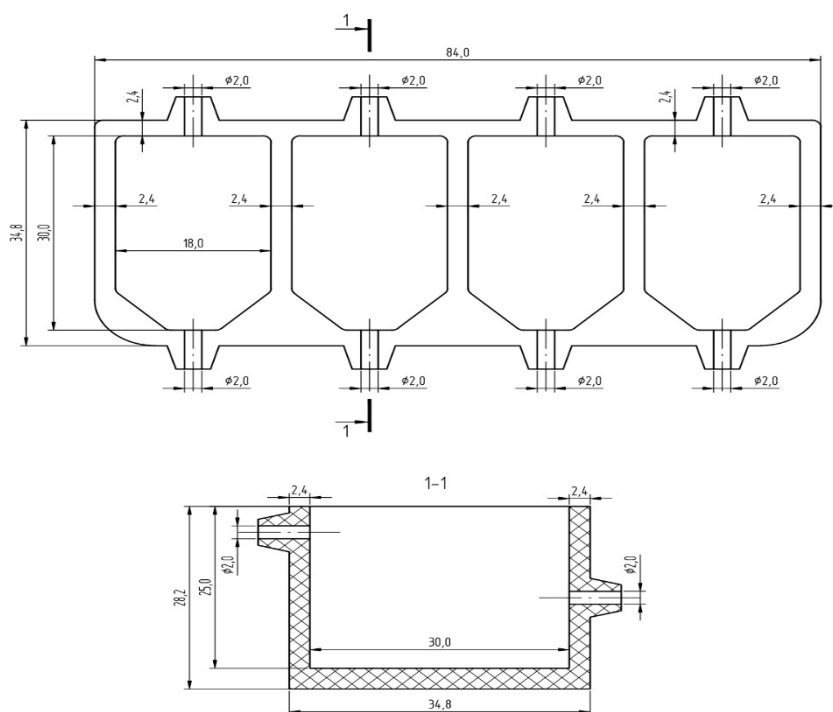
Чертеж блока с проточными ячейками (1). Вертикальный разрез проточной ячейки (1-1)
